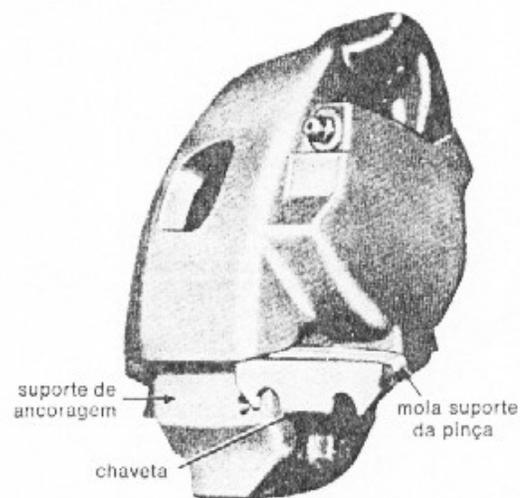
instalação da chaveta e mola no suporte de ancoragem
